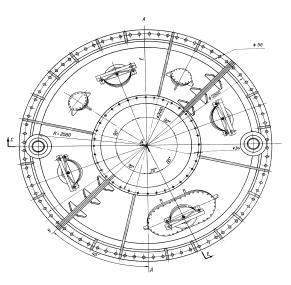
Засыпной аппарат колошника модели 3J I = Сторона наклочного мога B = Стык половин газового затвора D = Ос, доленной лечи и наклочного моста E = Стык части большого хонута
